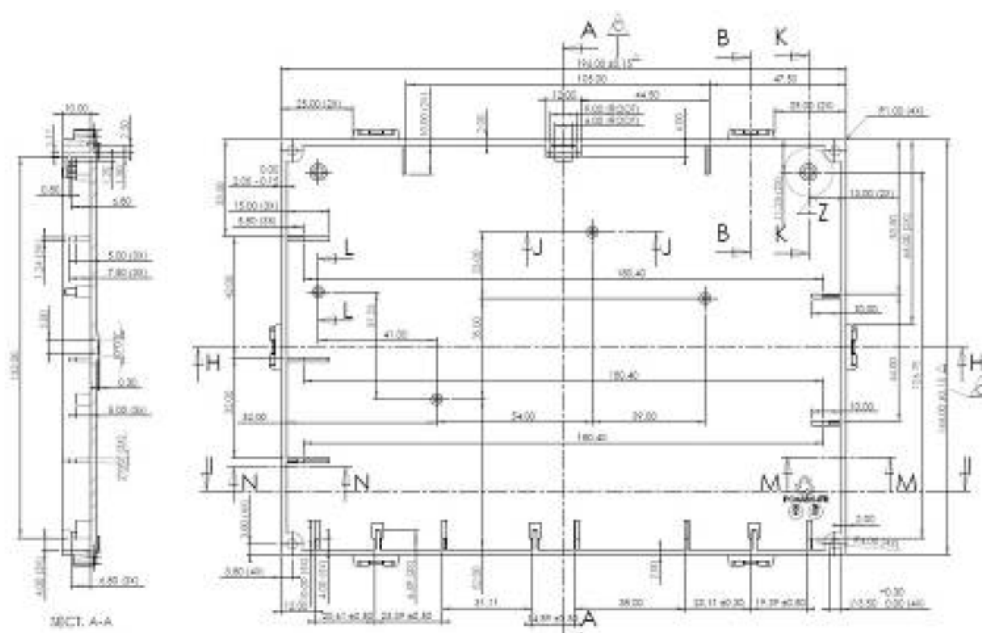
Внешний вид корпуса блока управления Honeywell S4966V2029
